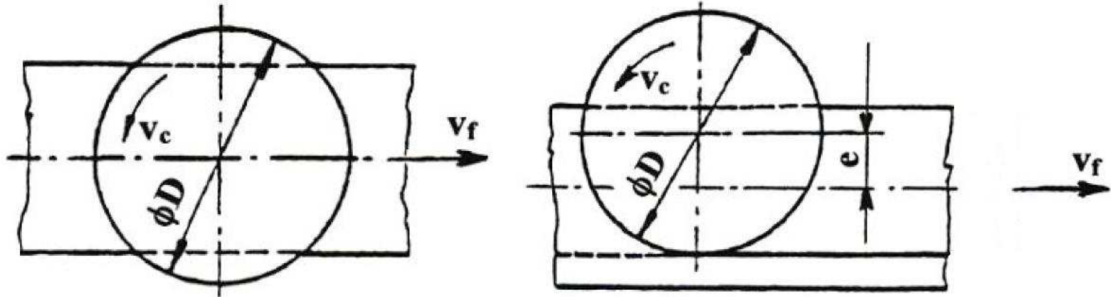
Druhy frézování [23]: válcové (vlevo); čelní (vpravo).
